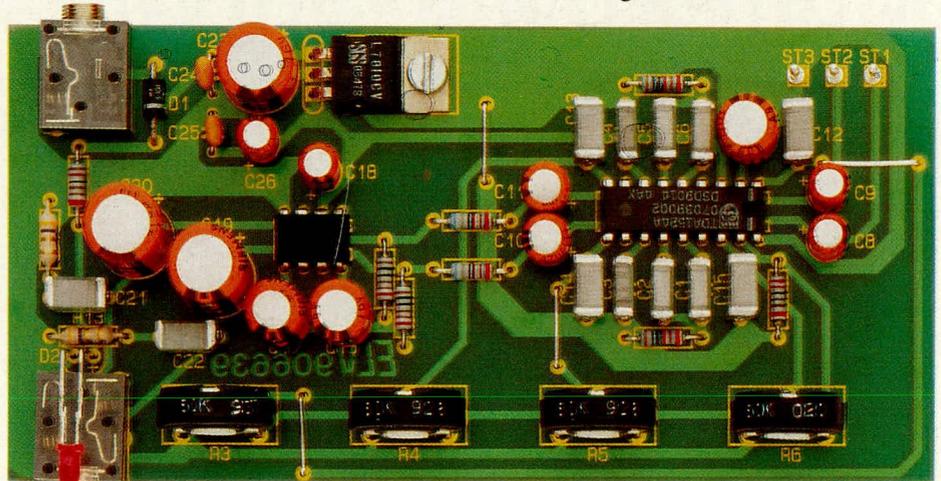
Einbaufertig aufgebaute Platine des TV-Kopfhörerverstärkers
